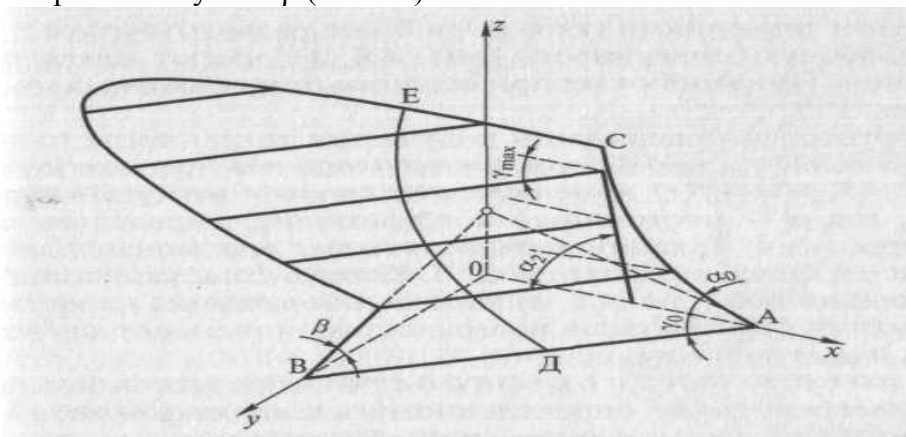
Схема образования рабочей поверхности корпуса плуга.
